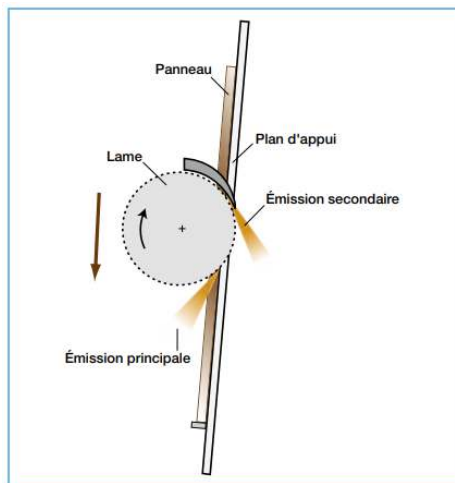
Émissions principale et secondaire d'une scie à panneaux
